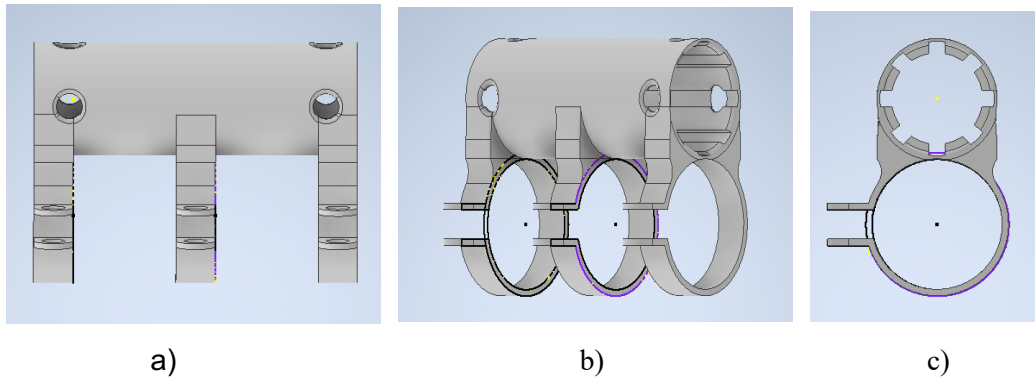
Diseño de soporte para el actuador Fuente. Diseño frontal literal a) vista inclinada literal b) vista lateral c).* elaborado por el autor.
